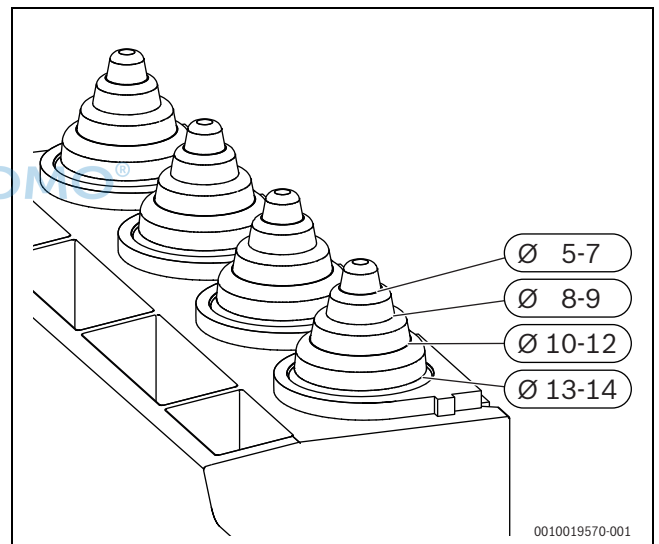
Zugentlastung an Kabeldurchmesser anpassen
